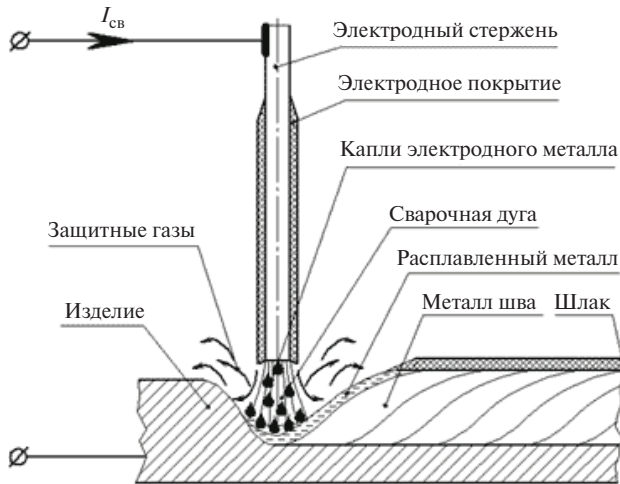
Схема сварки покрытым металлическим электродом [5]
